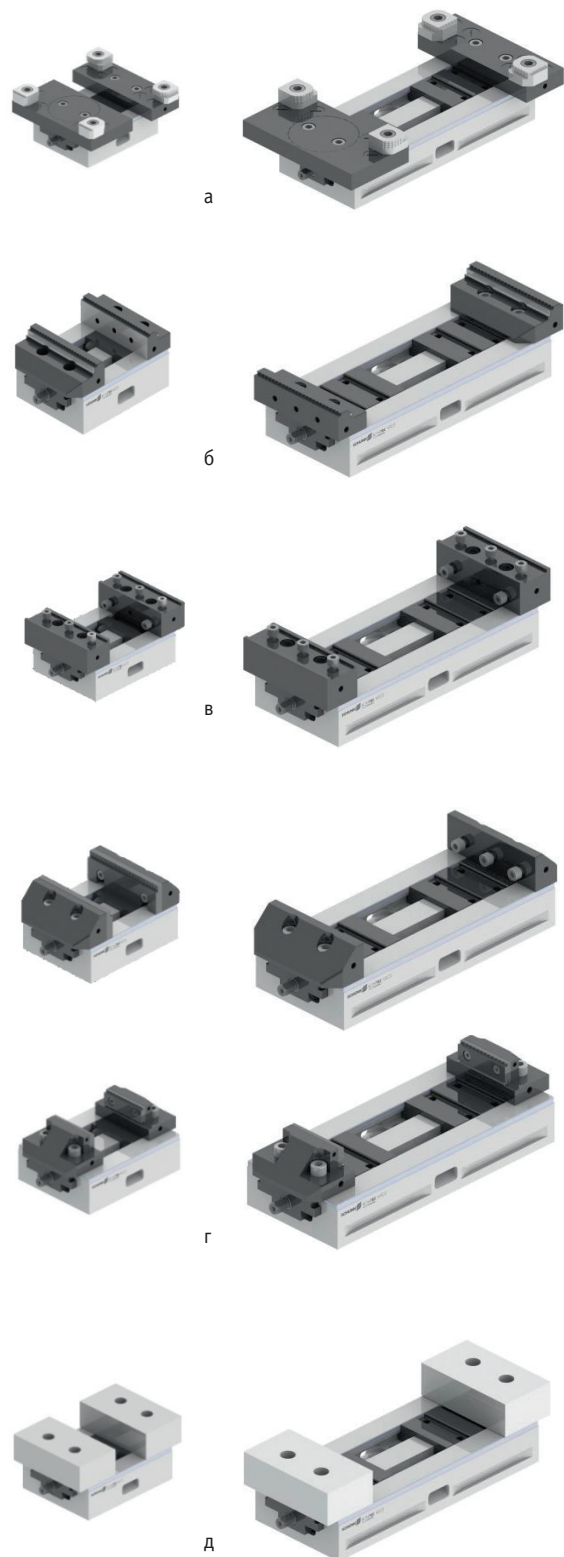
Возможные конструкции накладных кулачков тисков KSC: а – поворотная и адаптерная плиты, б – реверсивные кулачки, в – комбинированные кулачки, г – кулачки для 5-осевой обработки, д – алюминиевые кулачки
